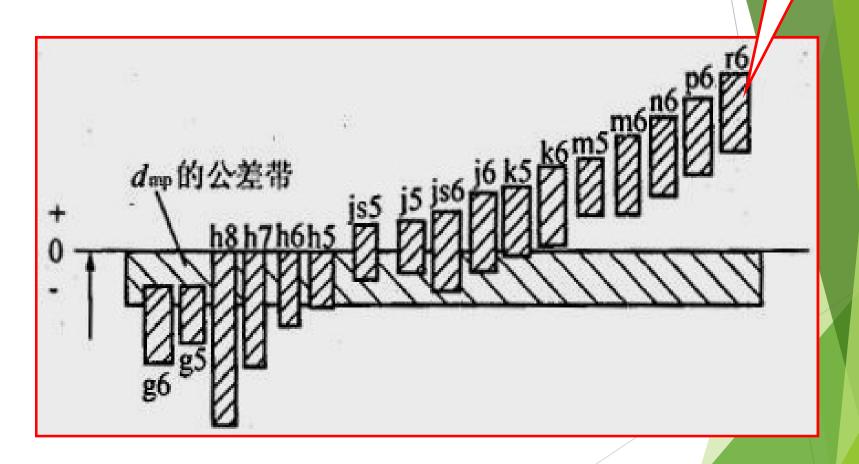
滚动轴承与轴和壳体孔的公差与配合
